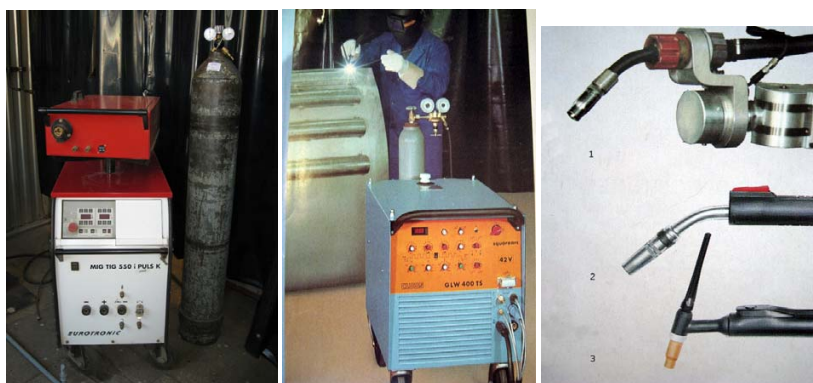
Пост ручной аргонодуговой сварки: а) общий вид; б) сварка неплавящимся электродом с присадкой; в) горелки для сварки
